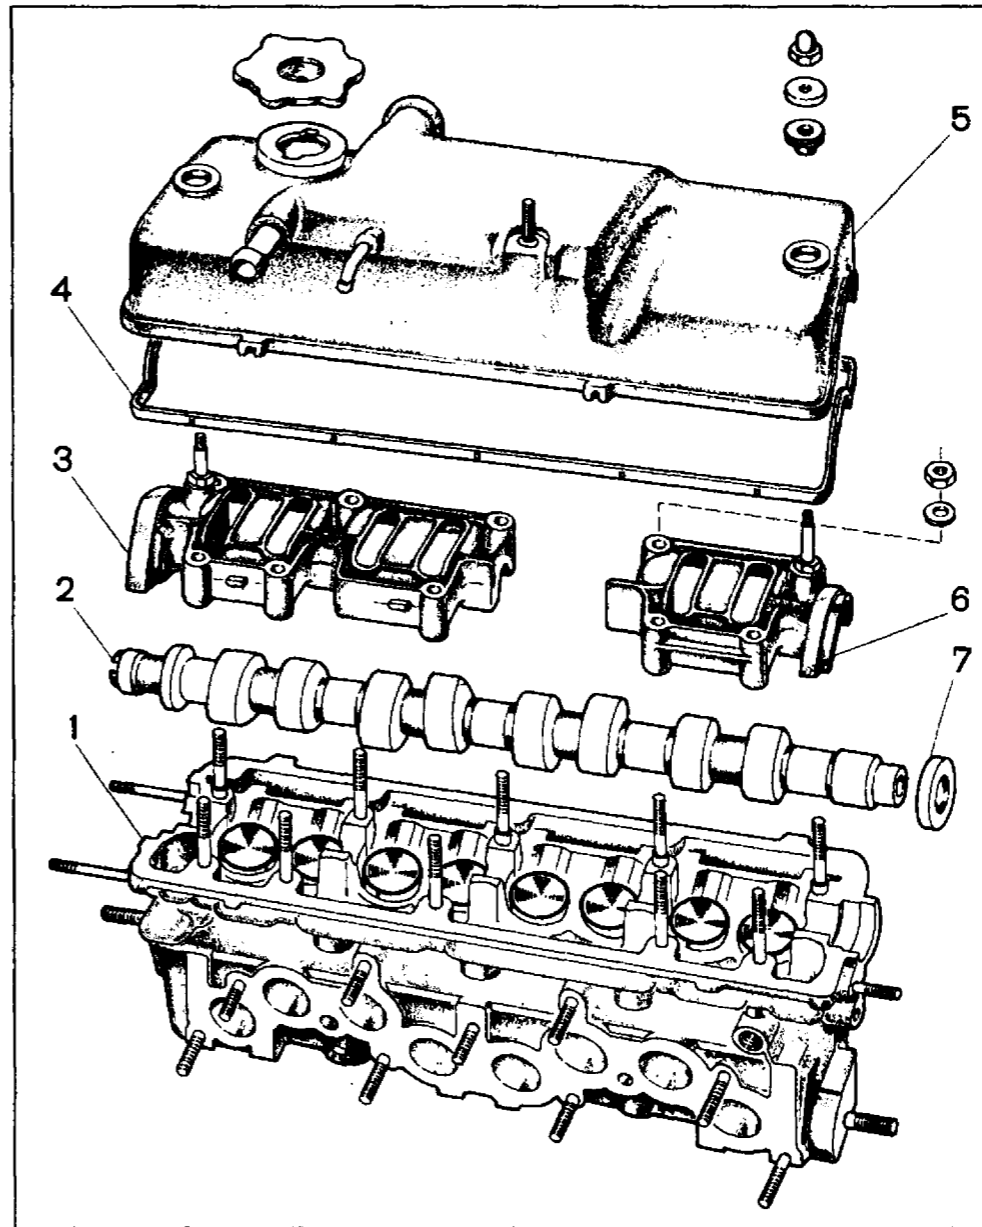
Разборка головки блока цилиндров: 1 — головка цилиндров; 2 — распределительный вал; 3 — задний корпус подшипников распределительного вала; 4 — прокладка; 5 — крышка головки блока цилиндров; 6 — передний корпус подшипников распределительного вала; 7 — сальник
